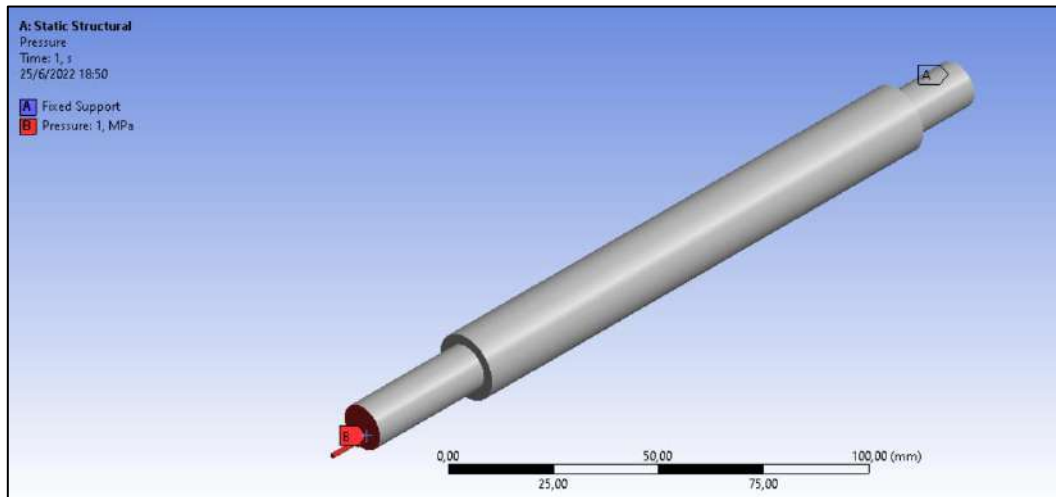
Aplicación de cargas y apoyos para el esparrago.
